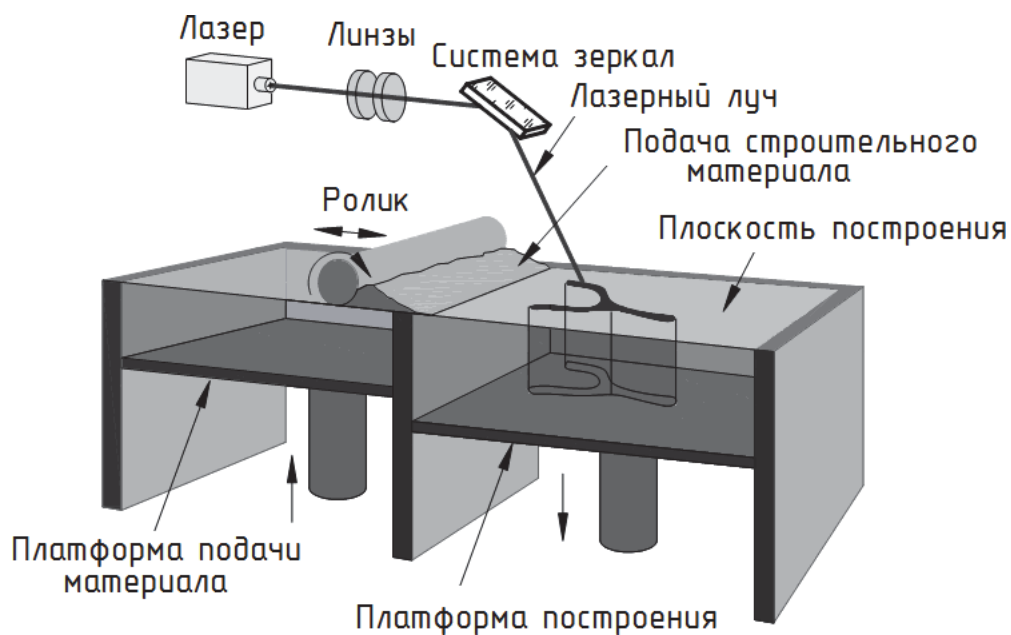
Схема получения детали путем объединения материала, распределенного на рабочей поверхности
